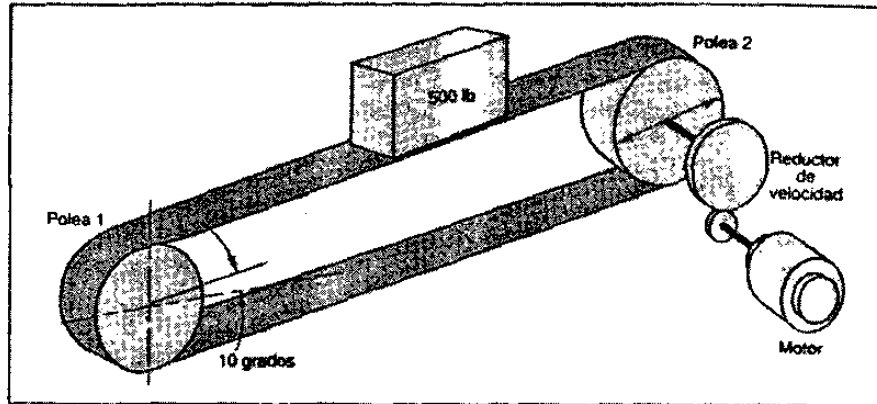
Ejemplo 2 – Transportador inclinado.
